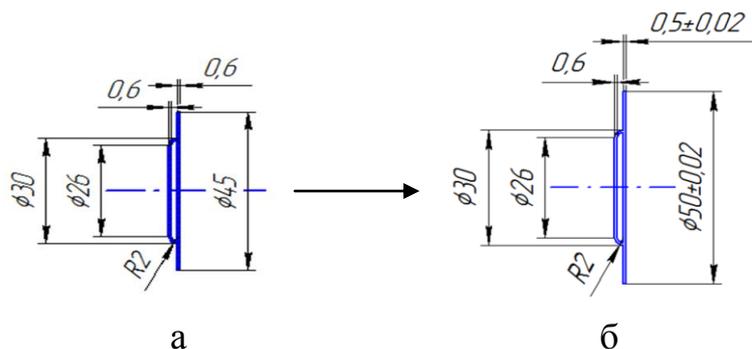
Заготовка корпуса подшипника электродвигателя:
